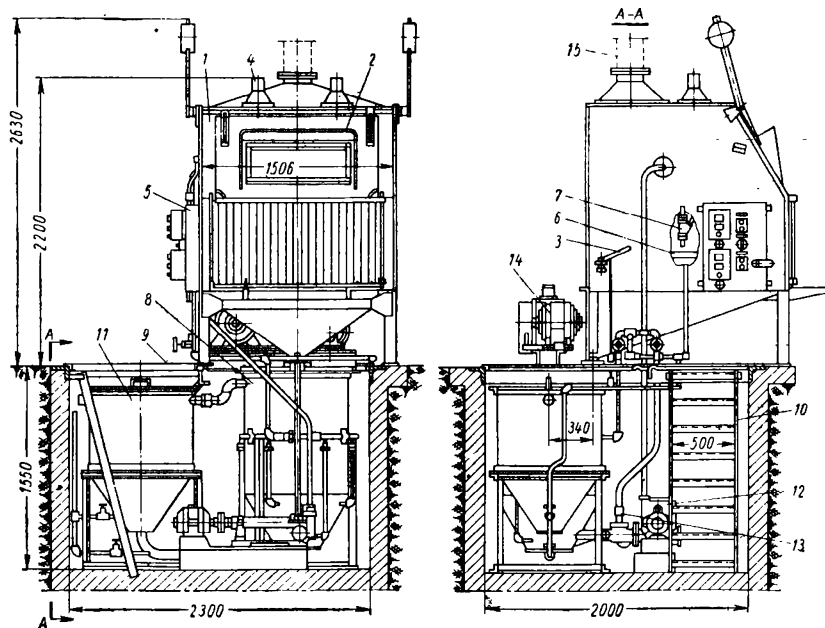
Гидропескоструйная установка: 1 — камера; 2 — дверца с резиновой завеской; 3 — ручка управления клапаном; 4 — фонарь; 5 — пульт управления; 6 — поворотный стол; 7 — пистолет; 8 — смеситель; 9 — настил из металлических листов; 10 — лестница; 11 — отстойник; 12 — насос для пульпы; 13 — трубопровод; 14 — привод смесителя; 15 — вытяжная труба
